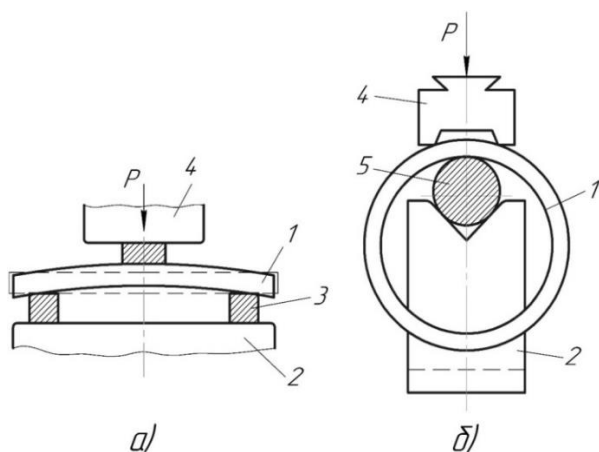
Схемы правки длинноосных (а) и кольцевых (б) поволоок:
